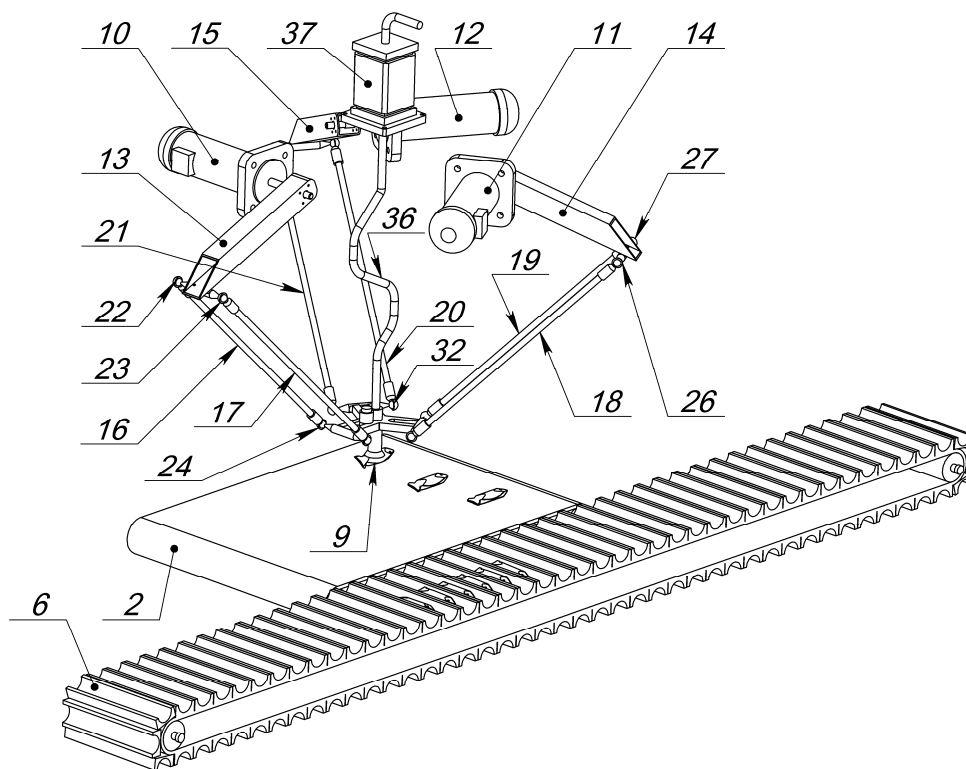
Схема расположения улавливающего приспособления и исполнительного привода относительно операционного и загрузочного конвейеров
